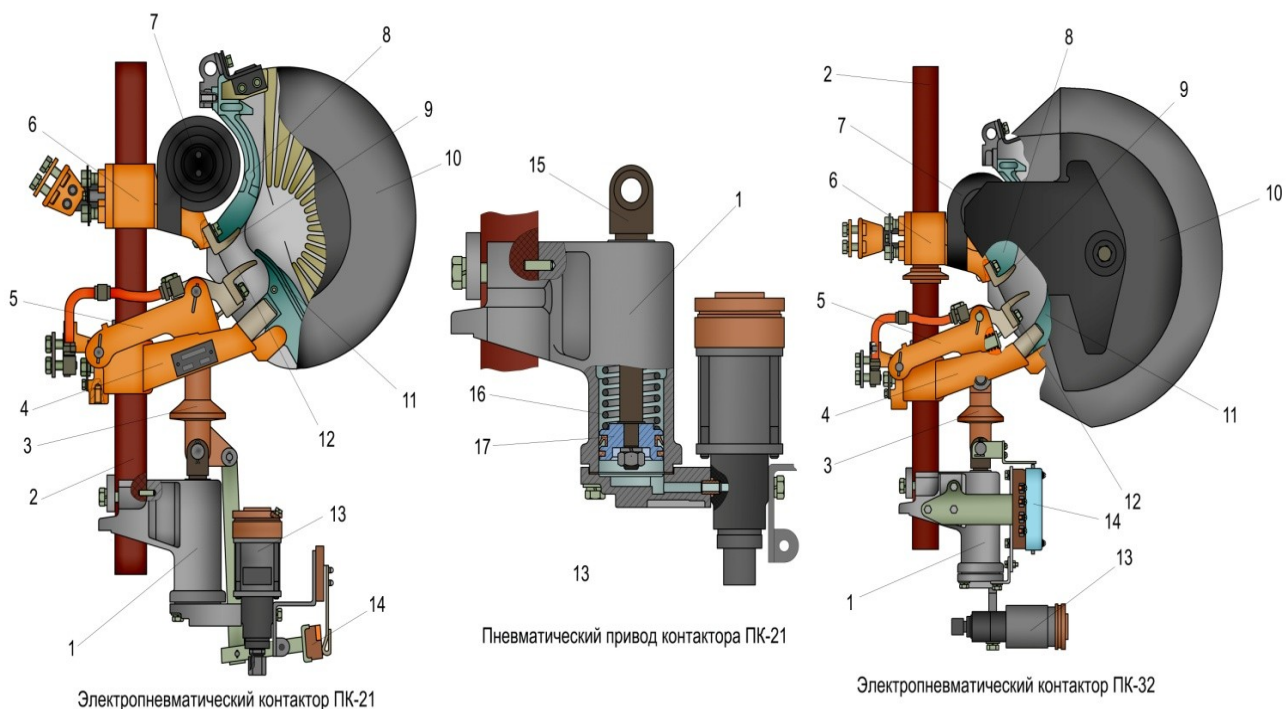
Элеktропневматический контактор ПК-21, ПК- 32
